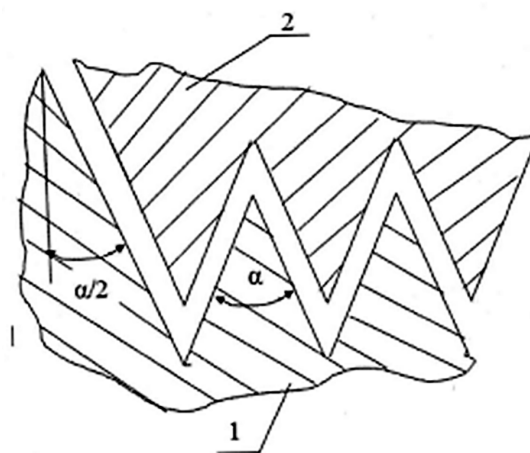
Схема выступов и впадин диспергатора: 1 – корпус; 2 – ротор
